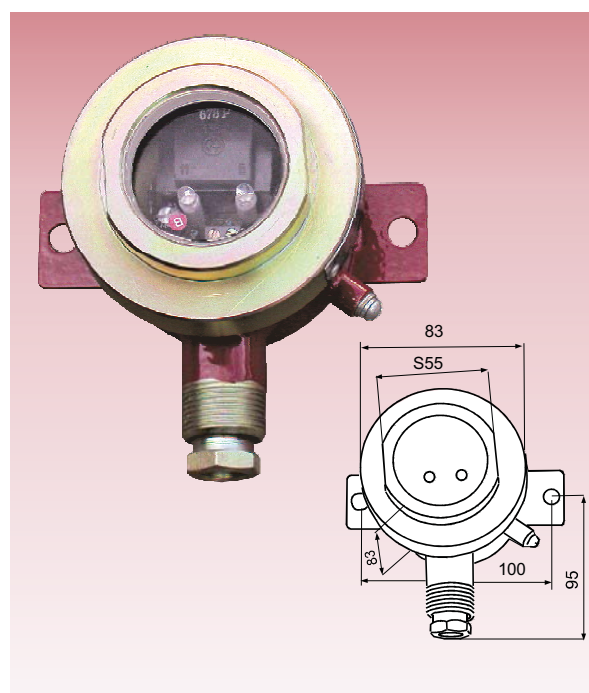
Сигнализатор ВУУК-МС. Внешний вид, габаритные и установочные размеры
